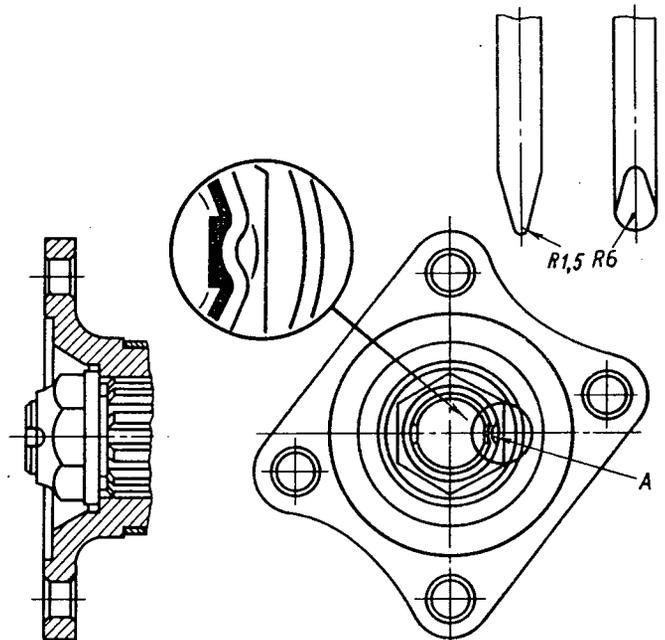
Absicherung der Mutter durch Einbiegen deren Kante in die Wellennut und Werkzeugprofil:
